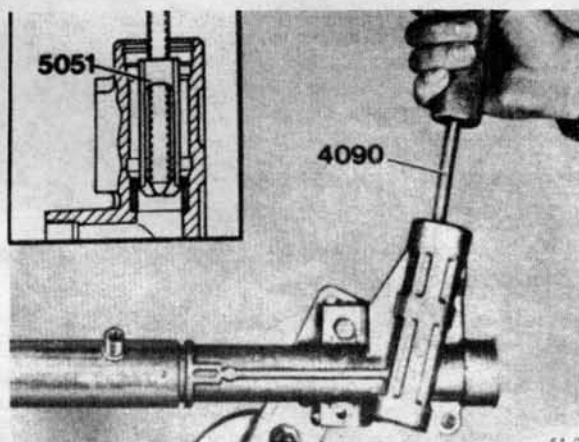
Снятие нижнего подшипника вала ведущей передачи и его уплотнителя
